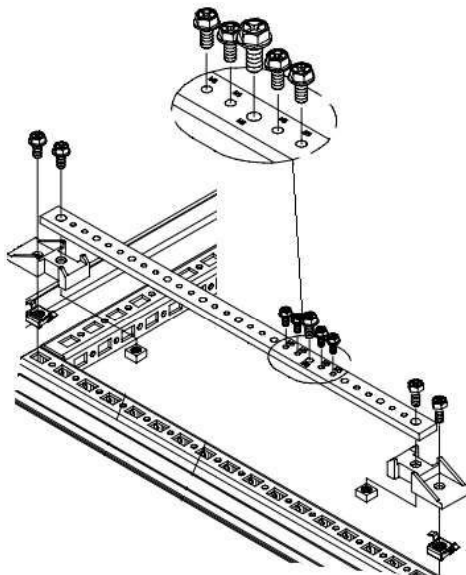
Detalle de montaje del Sistema de puesta a tierra.
